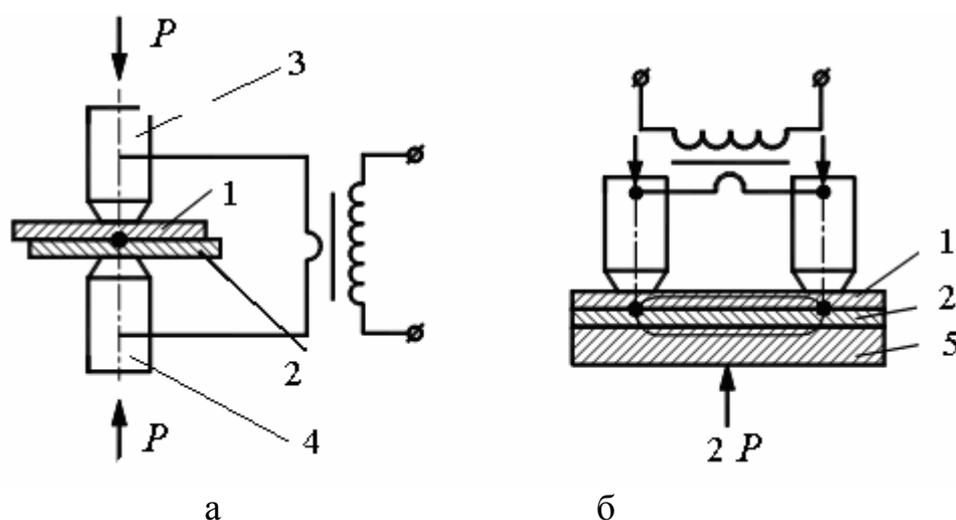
Принципиальная схема точечной сварки:
